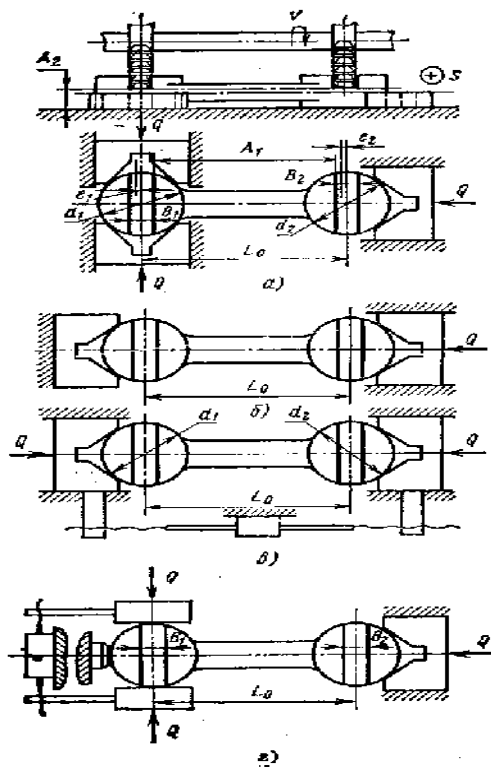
Схемы обработки поверхностей корпуса (к задаче 4)
